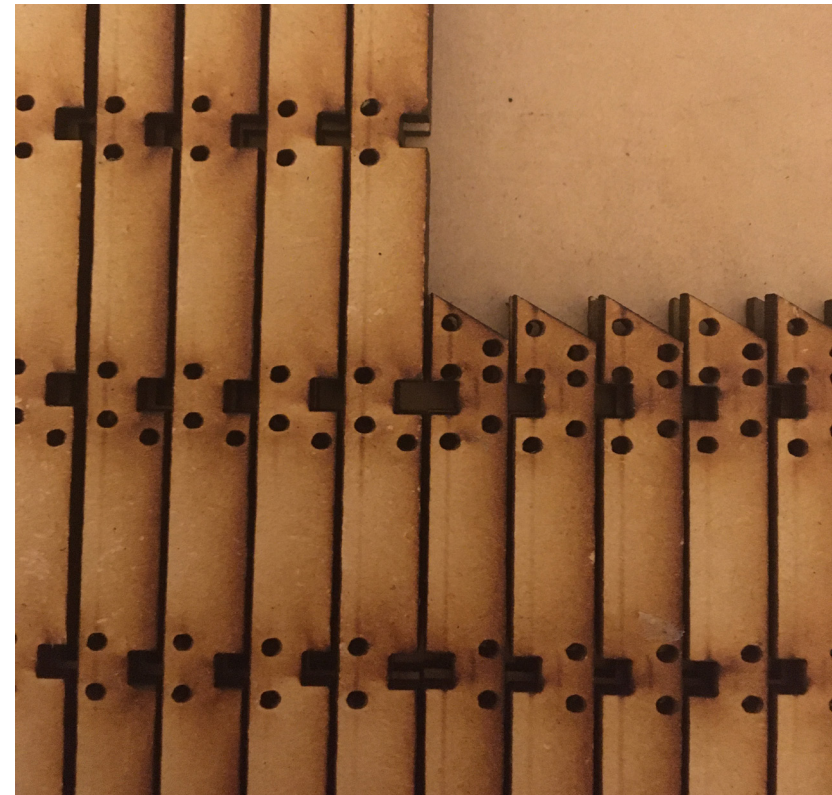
Ejemplo de reserva de piezas a escala para la elaboración de espacios habitables. Pilares maqueta final. Elaboración propia.
